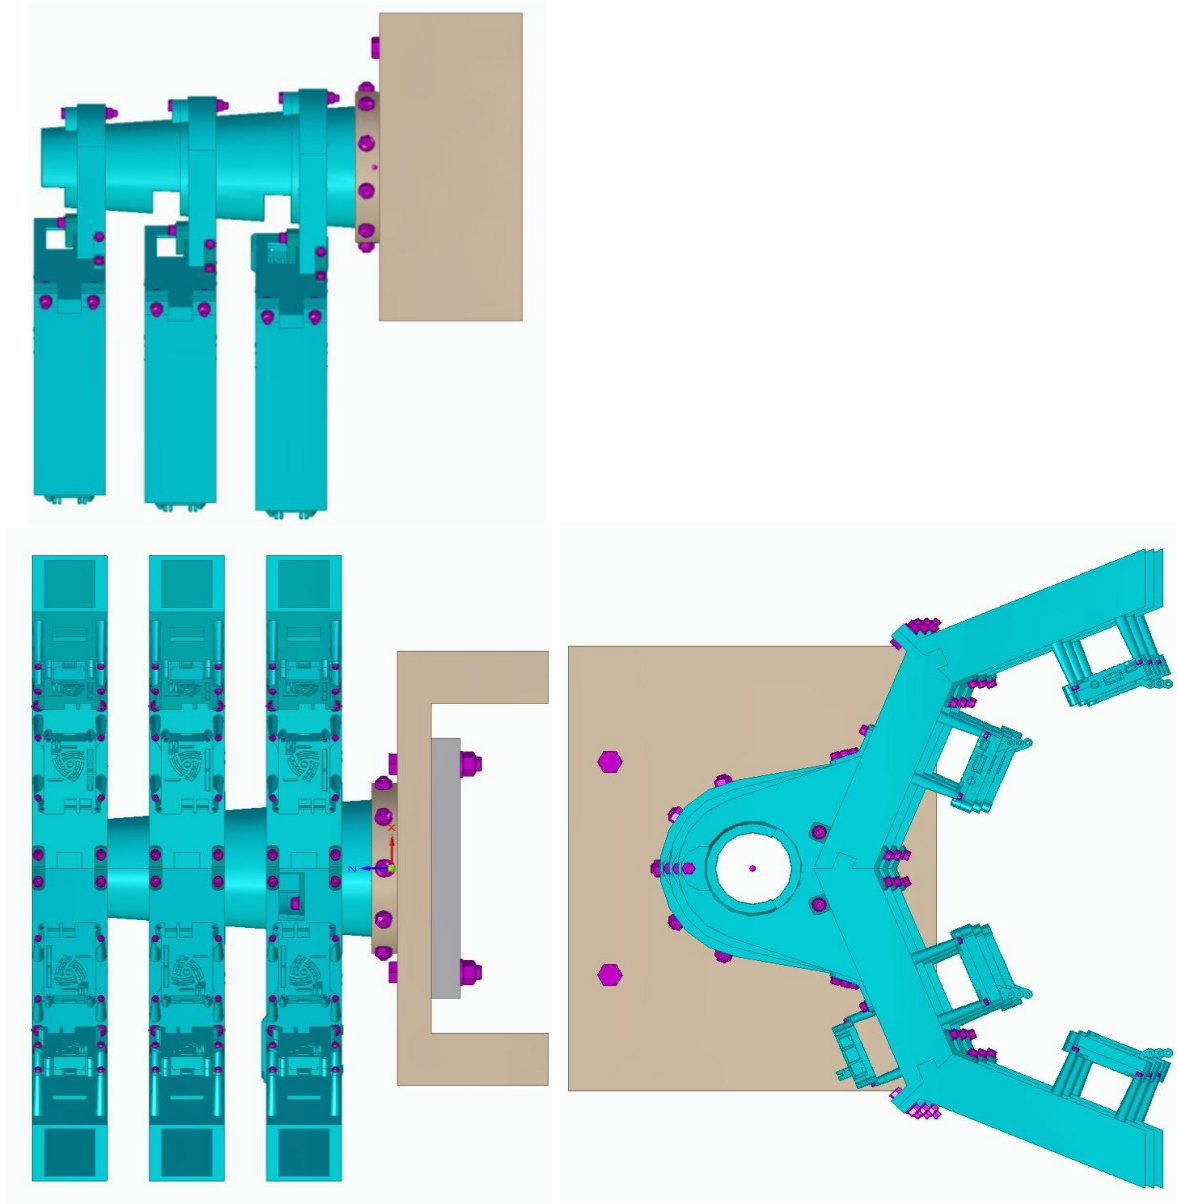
Alzado, planta y perfil de la solución propuesta para la estructura.
